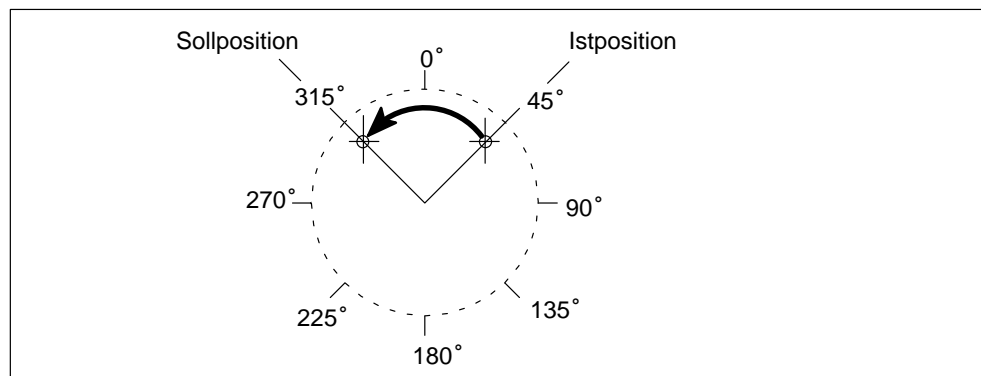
Rundachse auf kürzestem Weg bewegen
